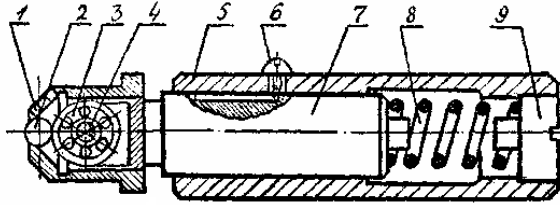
однокульовий пристрій обкату: 1 – сепаратор; 2 – куля; 3 – шарикопідшипник; 4 – вісь; 5 – корпус; 6 – упор; 7 – шток; 8 – пружина; 9 – гвинт
